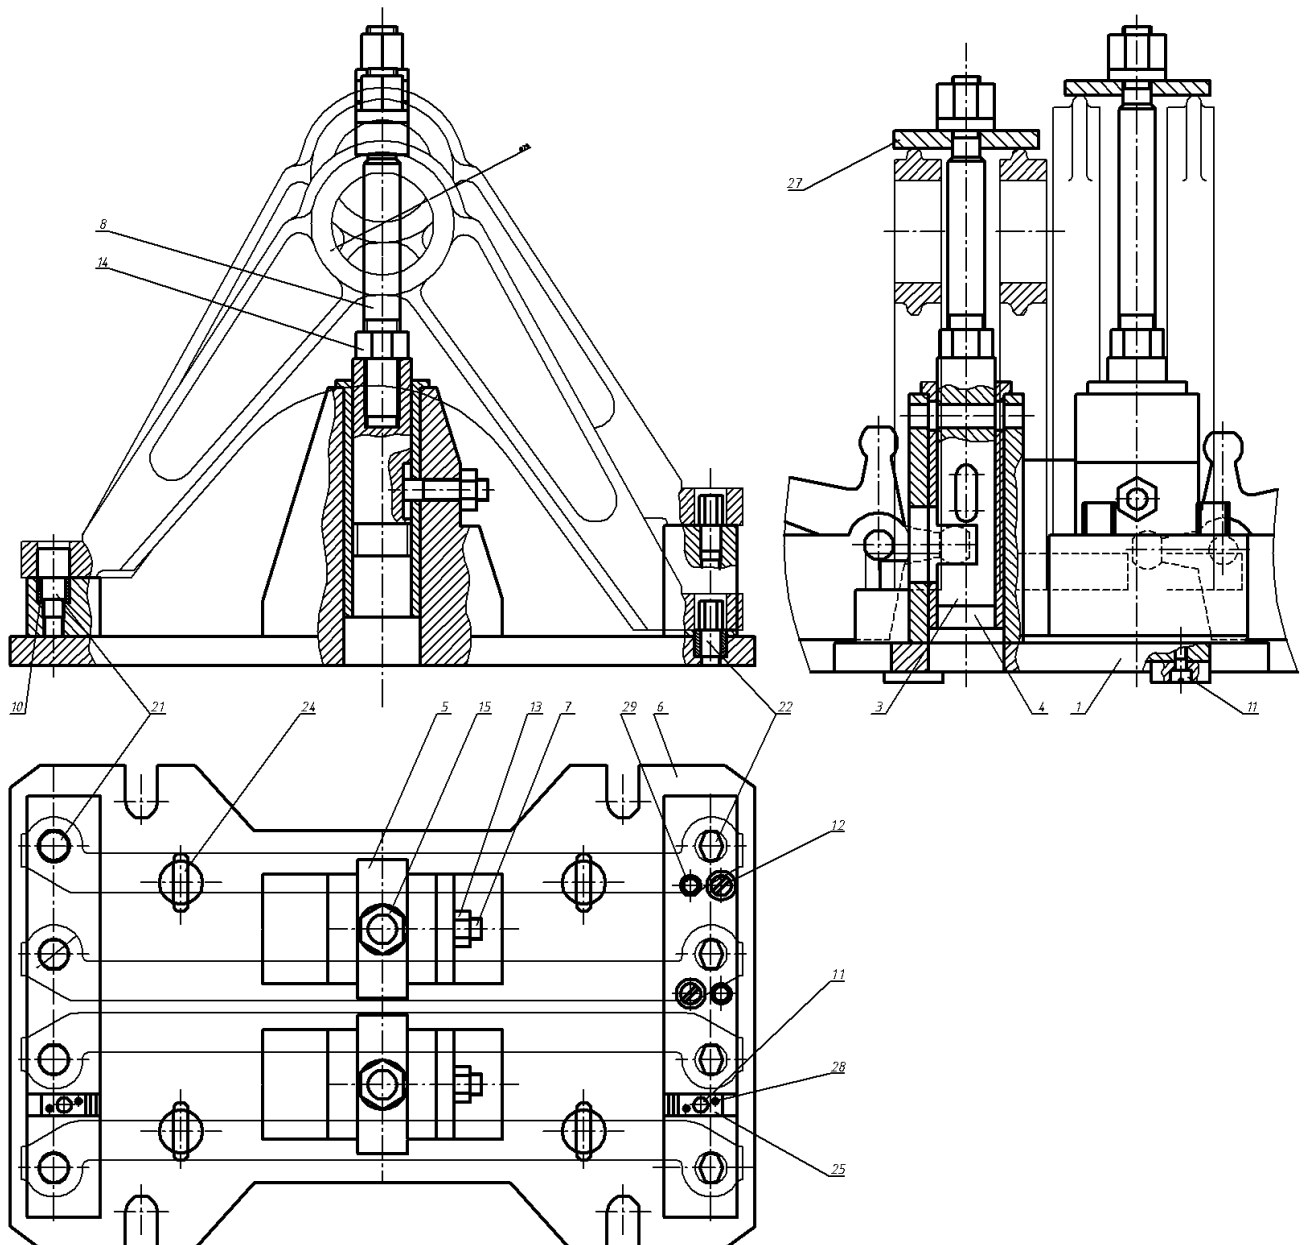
Пристрій чотиримісний для фрезерування деталі в розмір 25
